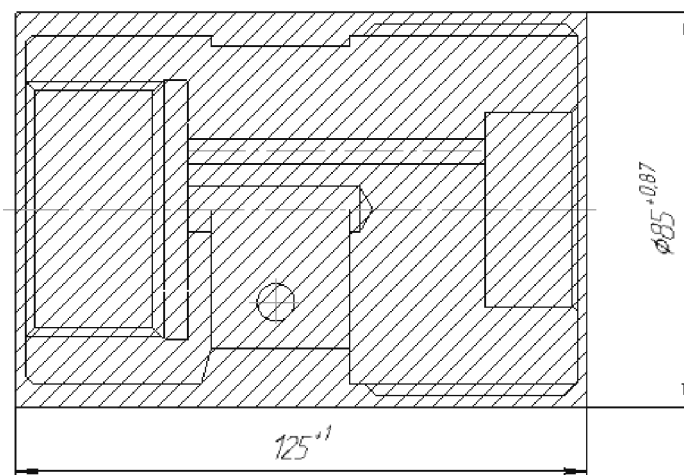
Ескіз заготовки, що виготовлена з прокату
